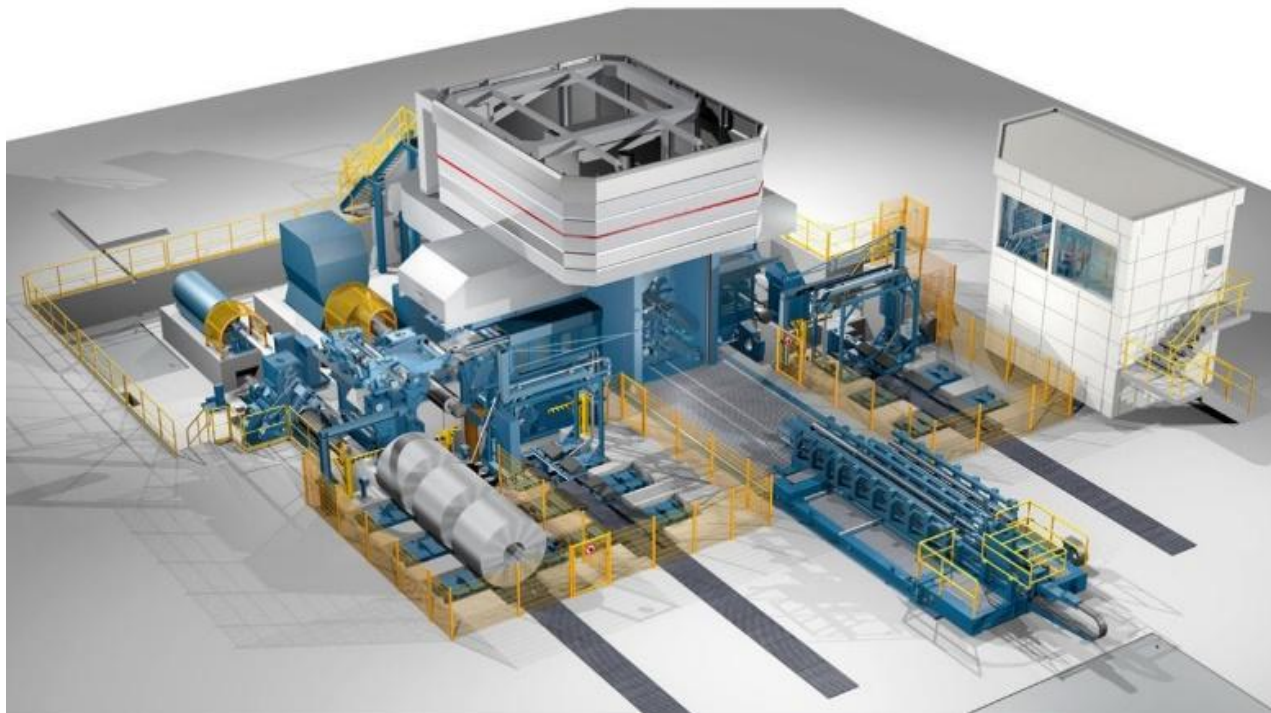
Комбинированный 4/6 валковый реверсивный стан
